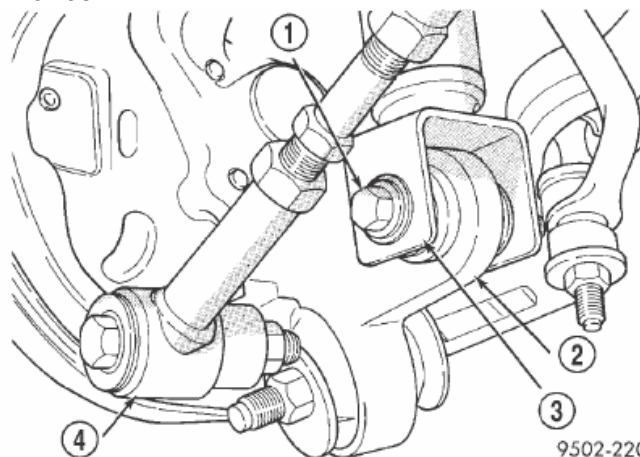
КРЕПЛЕНИЕ АМОРТИЗАТОРА К ШАРНИРУ ПОВОРОТНОГО КУЛАЧКА
